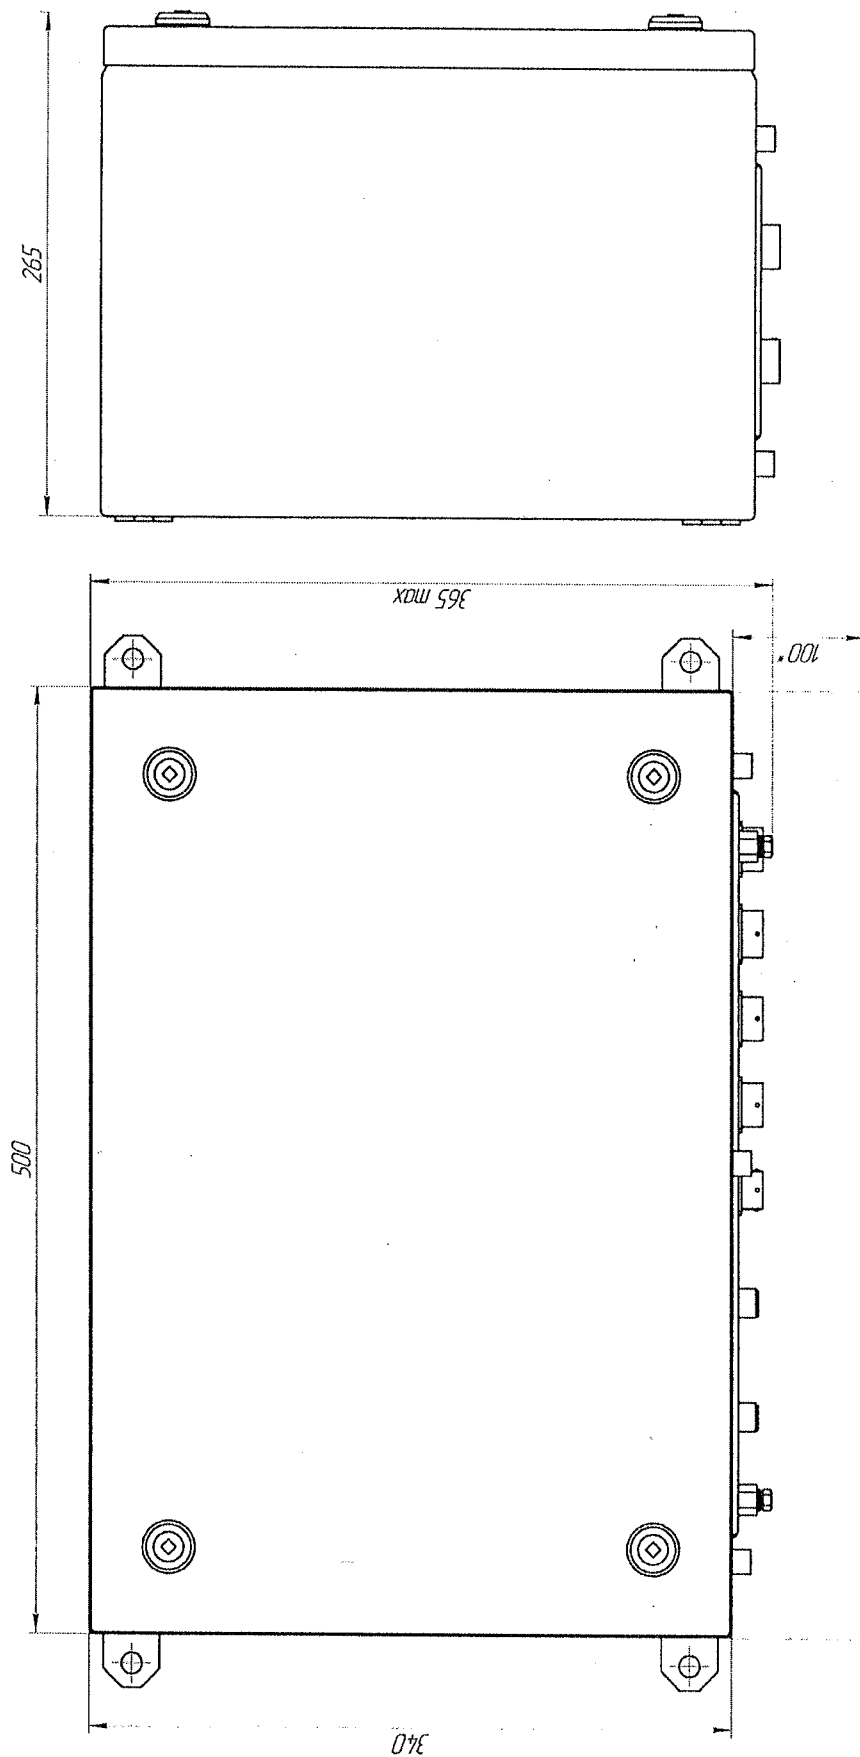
Внешний вид (вид спереди и слева) и габаритные размеры
